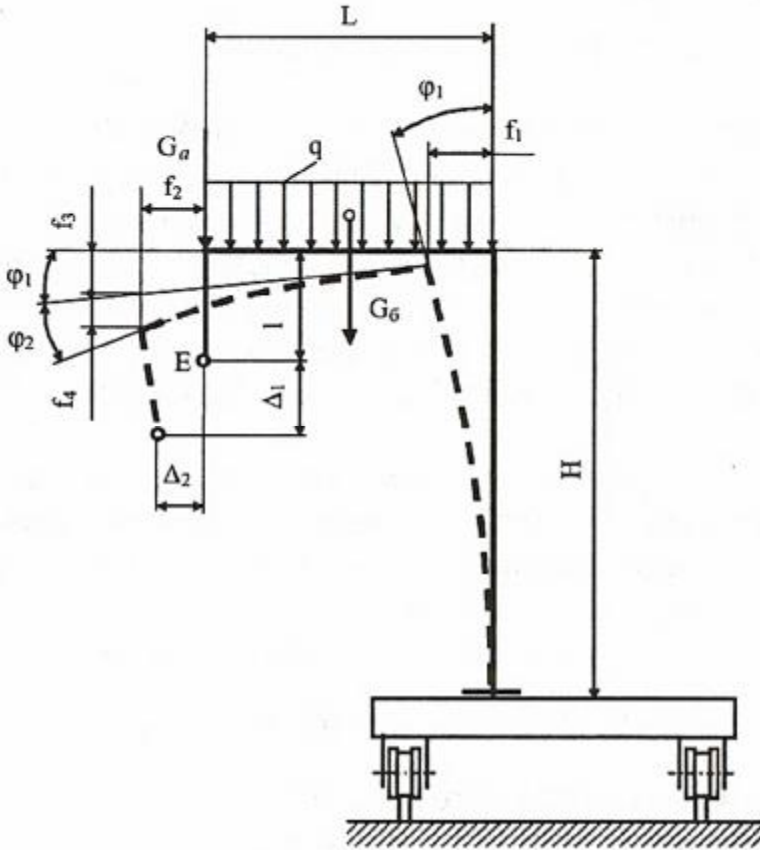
Розрахункова схема несучої конструкції глягольного зварювального візка [4]
